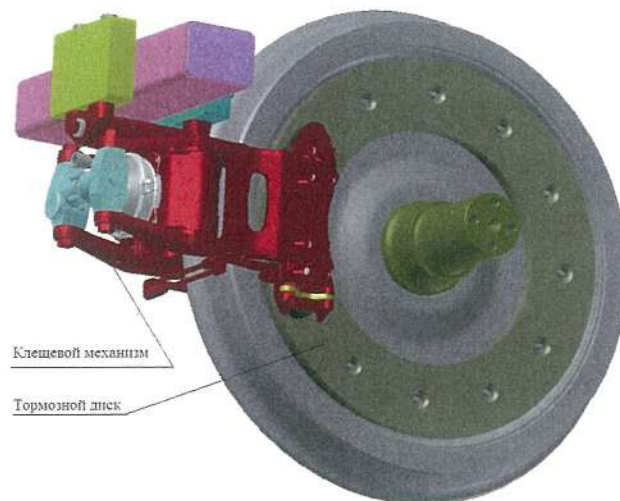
Дисковый тормоз, установленный на колесе колесной пары
